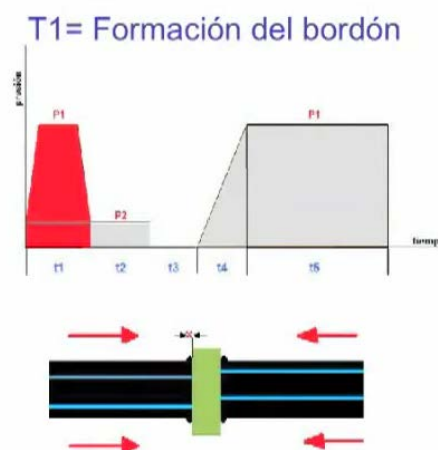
esquema del proceso de soldadura. Formación del bordón.
